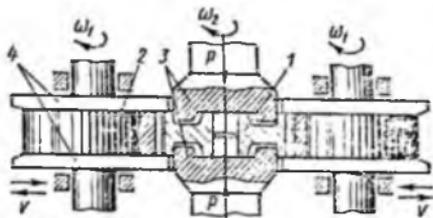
Формообразование зубьев шестерен прокаткой с радиальной подачей валков
